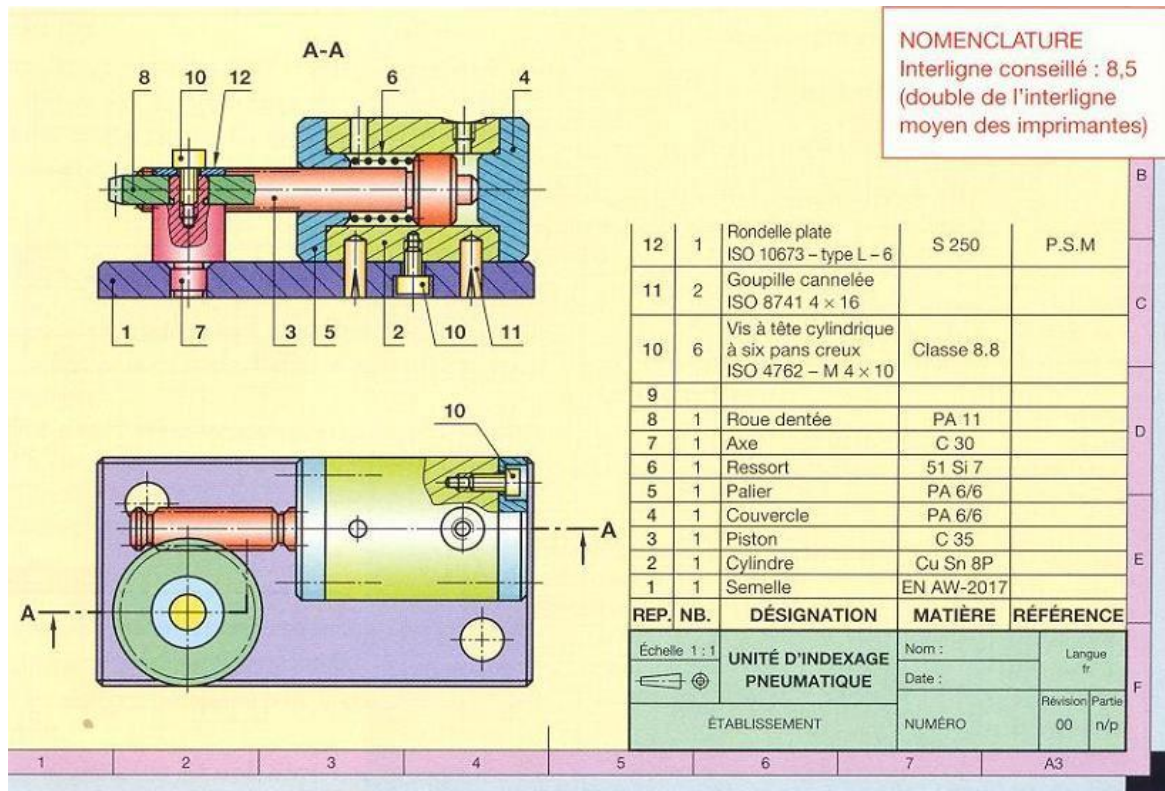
Dessin d'ensemble, Cartouche, Nomenclature.
